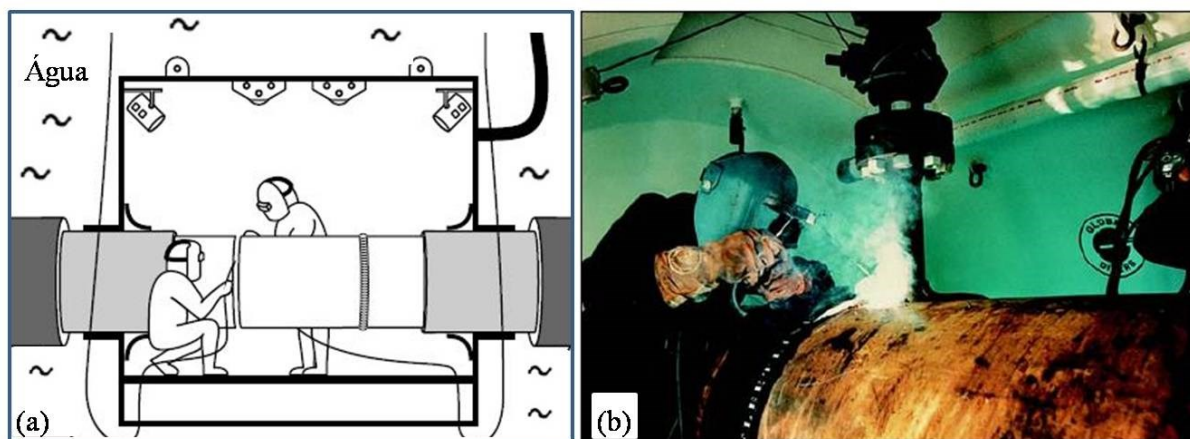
Técnica de soldagem subaquática hiperbárica: (a) desenho esquemático e (b) Soldador / Mergulhador trabalhando dentro da câmara para soldar um duto ramificado.
